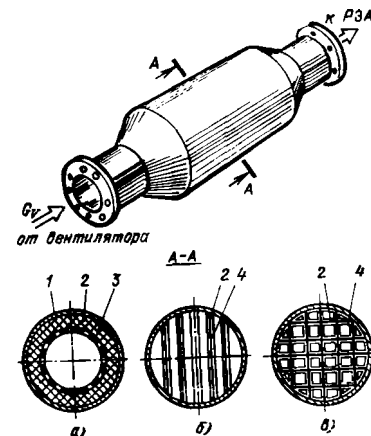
Конструкция глушителя шума: а — трубчатого типа; б — пластинчатого типа; в — сотового типа; 1 — корпус глушителя; 2 — звукопоглощающий материал; 3 — сетка; 4 — разделительная перегородка
